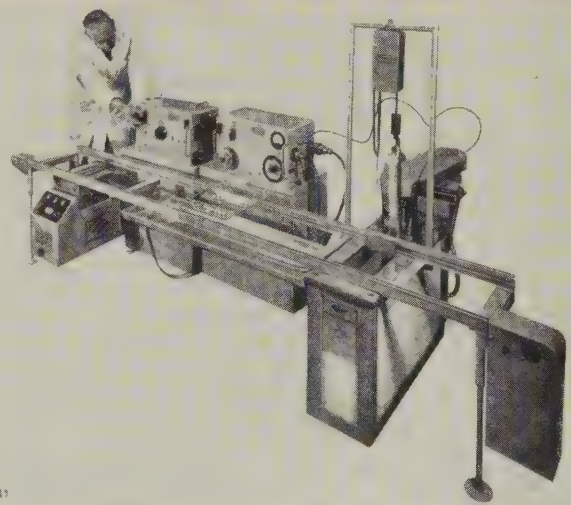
Flowsolder-Maschine für das Verlöten von gedruckten Schaltungen.
